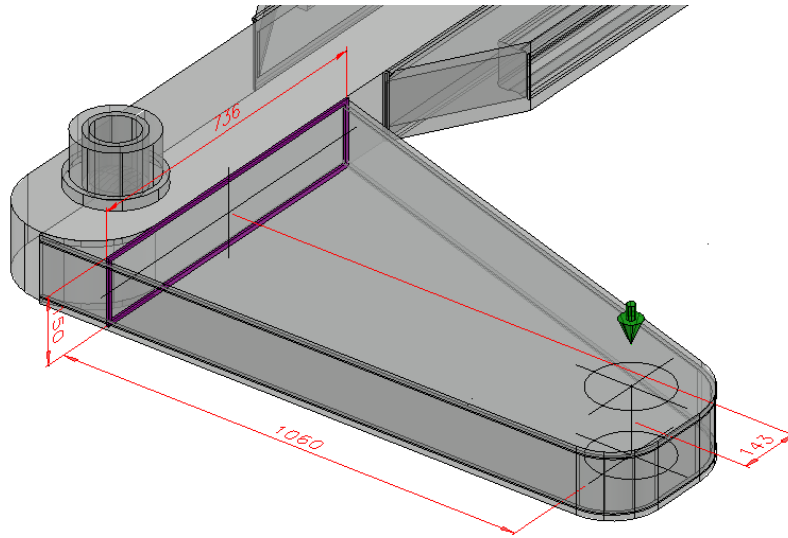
Esquema de soldadura y carga en extensión lateral de zapata.
